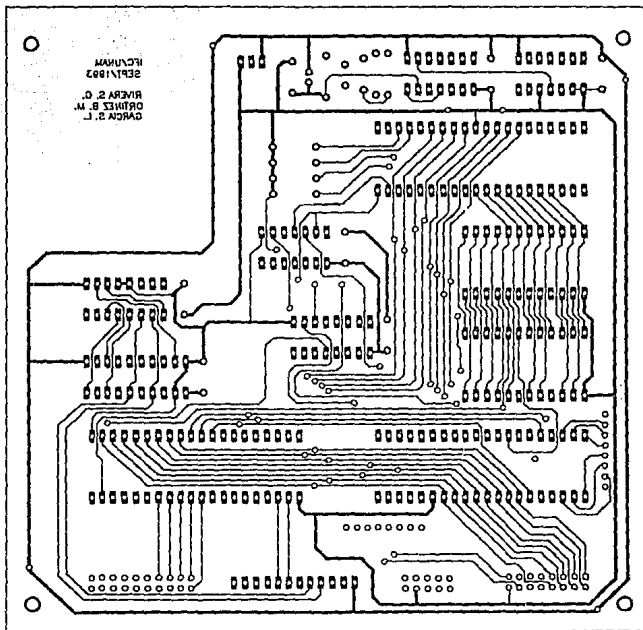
Cara de soldadura de la tarjeta de control.
